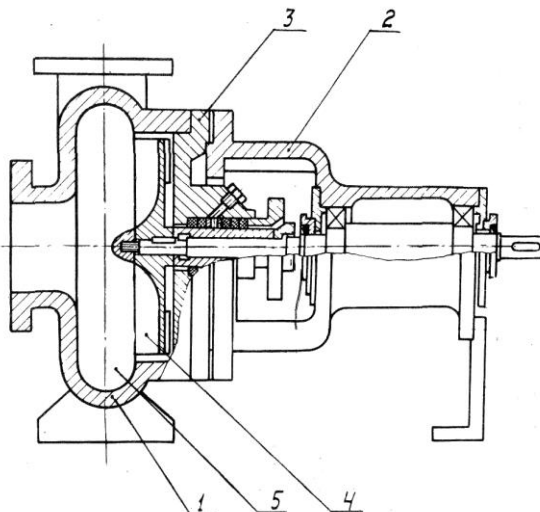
Вільновихровий насос «Туго»: 1 - корпус; 2 - вузол опорного кронштейна; 3 - корпус ущільнення; 4 - робоче колесо; 5 - вільновихрова камера
